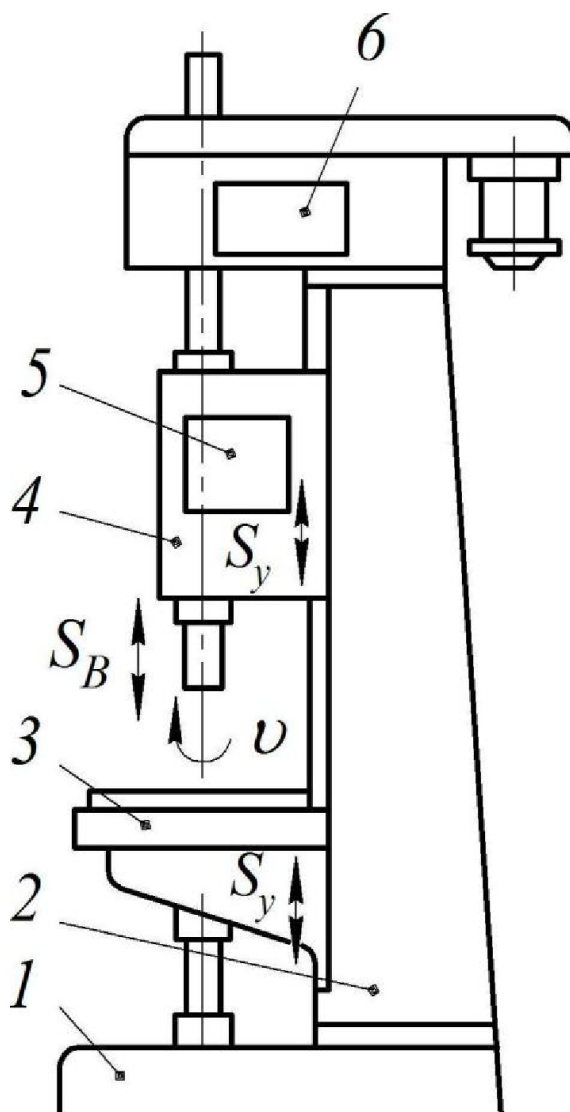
Загальний вигляд вертикально-свердлильного верстату
